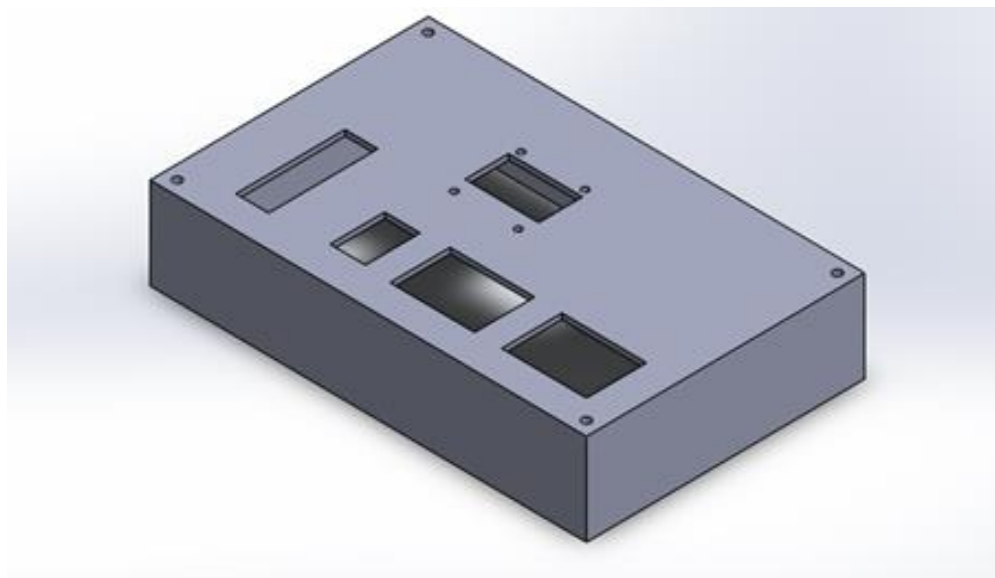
Diseño de parte superior de la carcasa en SolidWorks [Los autores].
